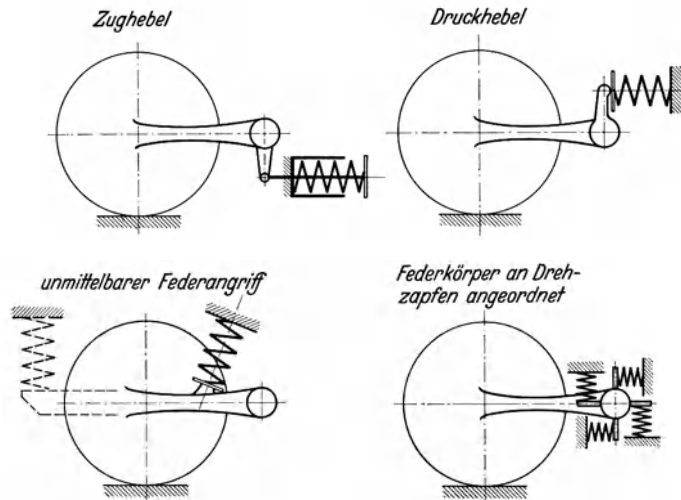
Schraubenfeder an Längshebel-Radaufhängung.
